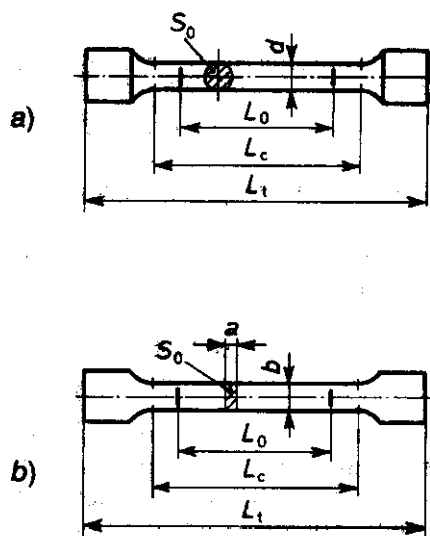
Provini per prove di trazione: a) sezione circolare; b) sezione rettangolare
